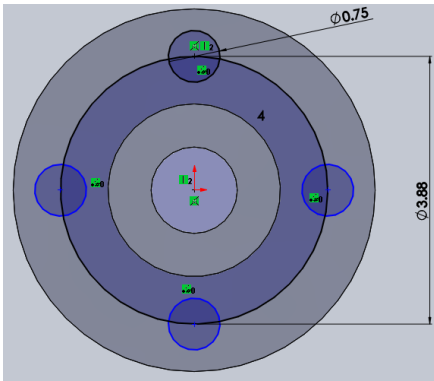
Dimensionamiento de la boquilla en el lado de la coraza. Fuente: SolidWorks
